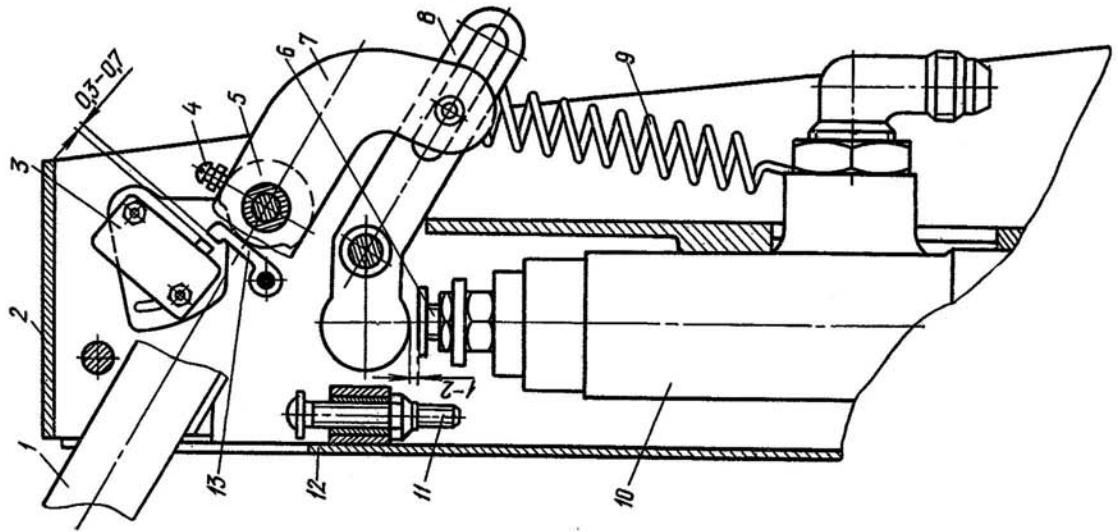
Установка клапана аварийного торможения УГ-100У:
